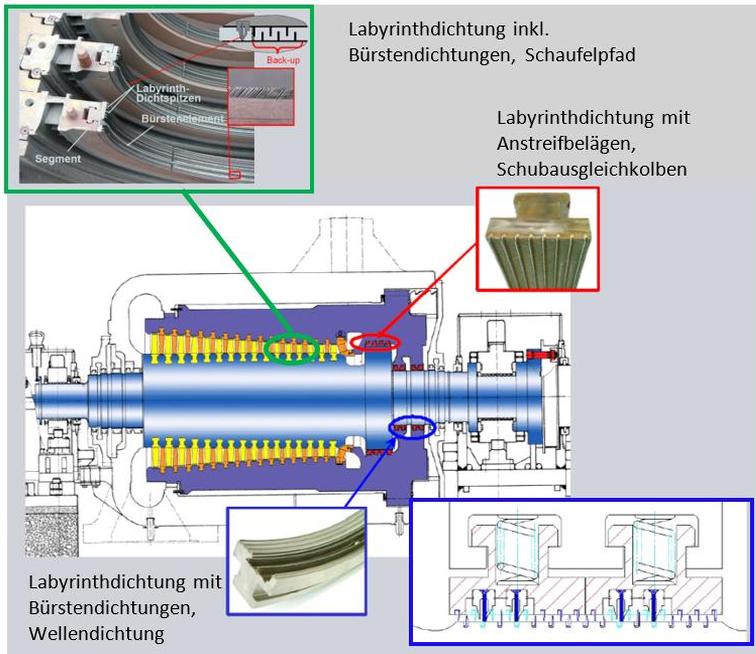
Bürstendichtungen in einer Turbomaschine
